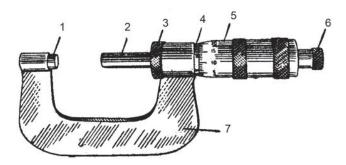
Микрометр для наружных измерений: 1 — пятка; 2 — микрометрический винт; 3 — стопорная гайка; 4 — втулка; 5 — барабан; 6 — трещотка; 7 — скоба
